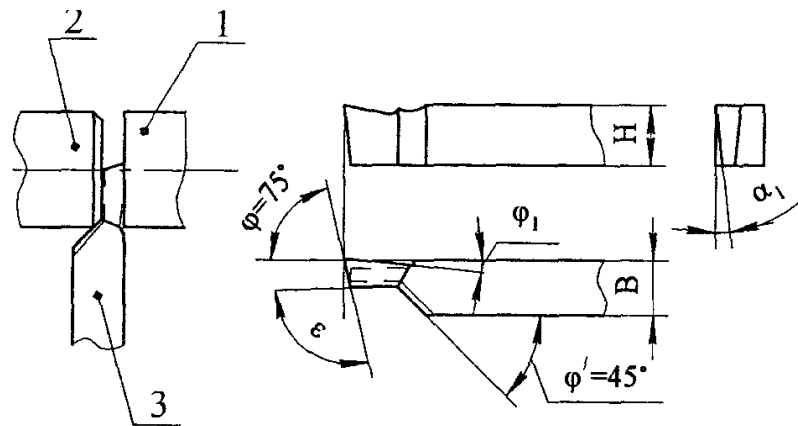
Різець для відрізки деталі від пруткової заготовки: 1 відрізається деталь; 2 - пруткова заготовка; 3 - допоміжне лезо
